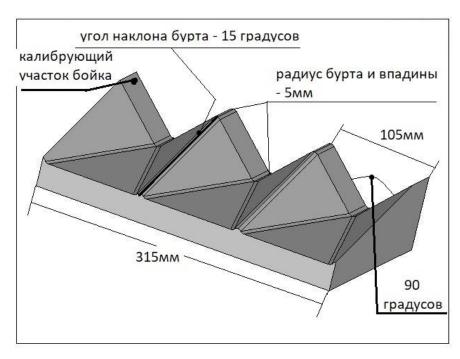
Рисунок бойка с размерами для получения трех сортовых заготовок
